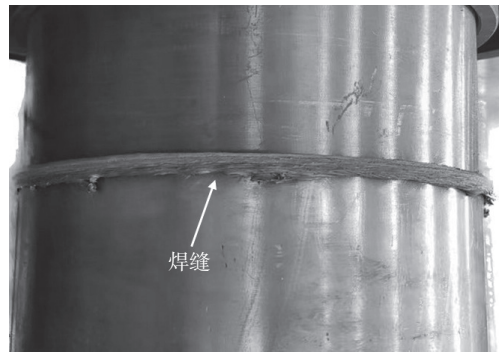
TA18 管摩擦焊接接头的宏观形貌
